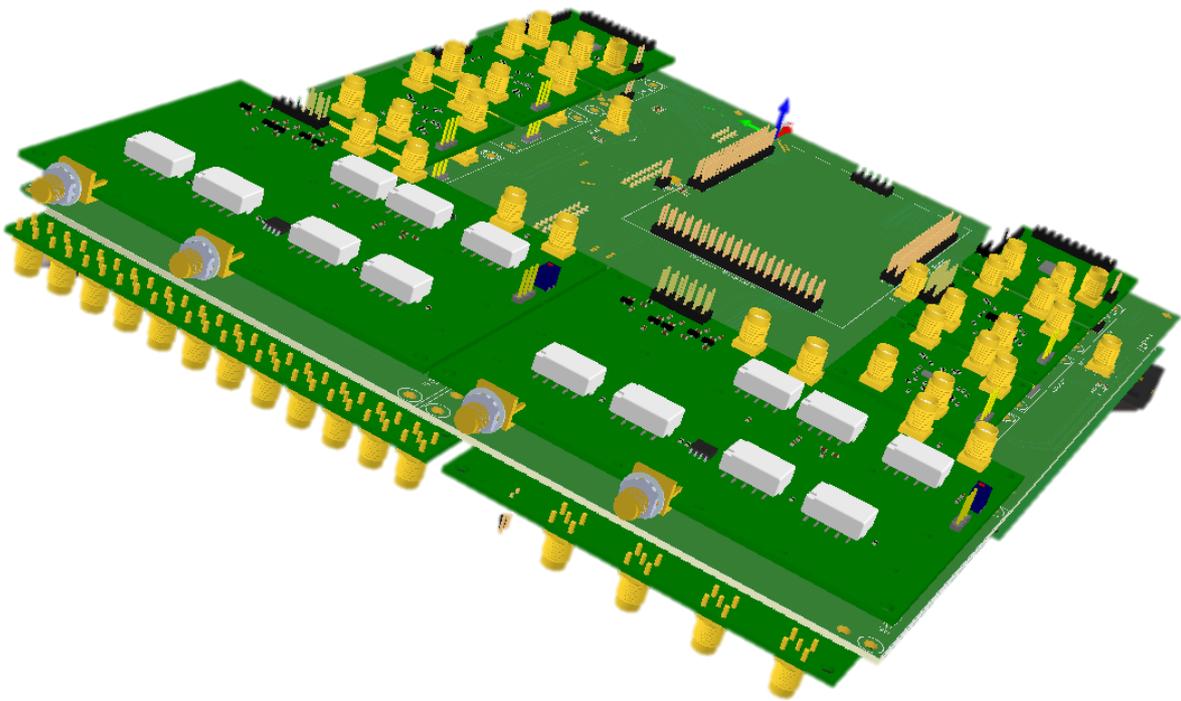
PCB 3D Sistema final (placa-mãe)
